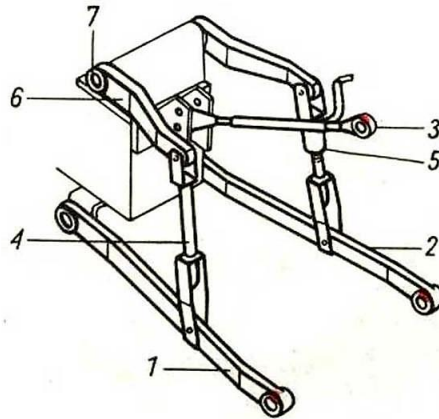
Attelage trois-points du tracteur : 1,2 - bras inférieurs, 3 - barre supérieure, 4 - bielle de relevage gauche, 5 - bielle de relevage droite à longueur réglable, 6 - bras de levage, 7 - arbre de levage
